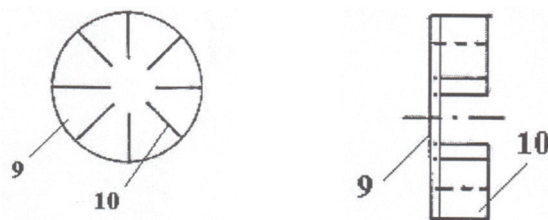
,5. Вид спереди и вид слева (с установленными на колеса) дисков с лопастями
